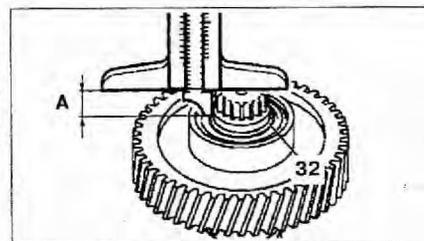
Измерение расстояния А от конца промежуточного вала до блокировочного кольца 32 с помощью штангенциркуля.
